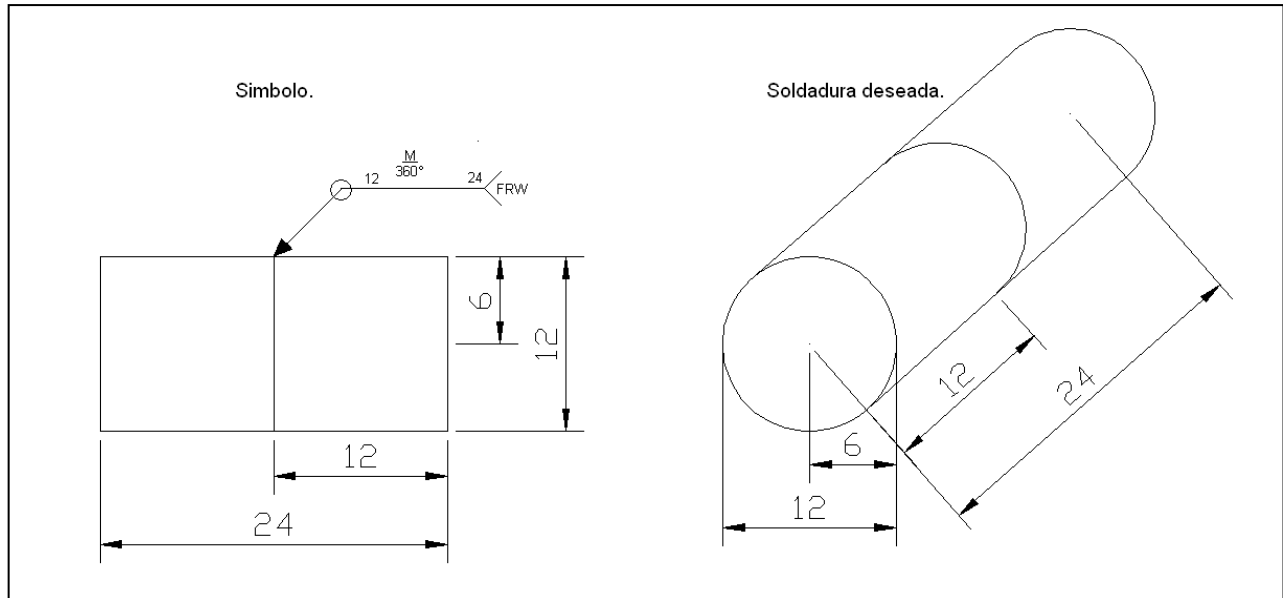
Ejemplo de pieza de aluminio soldada (flecha), por el método de fricción, diagrama de soldadura y símbolo de esta.
